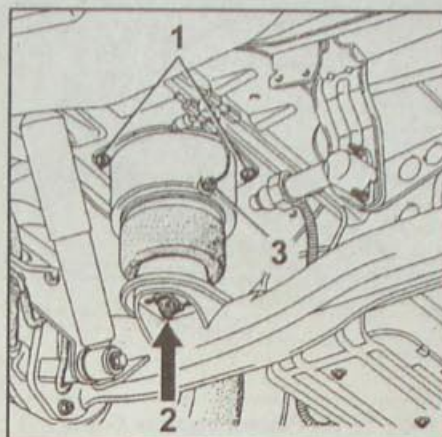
Расположение гайки (2) нижнего крепления и болтов (1) верхнего крепления пневматической рессоры к чашке кузова и штуцера для подачи сжатого воздуха (3)
